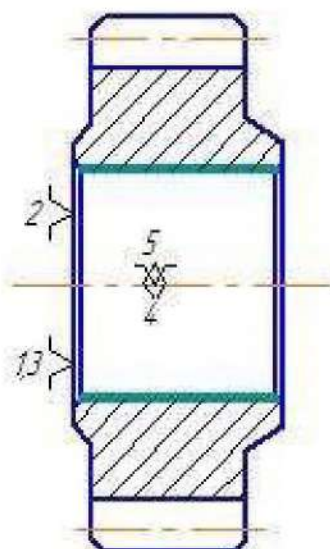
Схема базування заготовки на токарній операції 010
